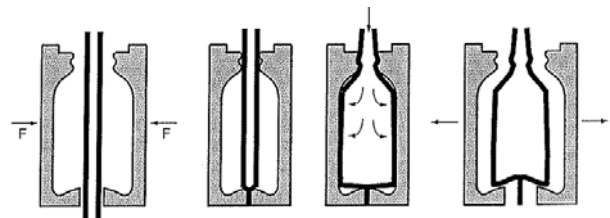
Extrusion-soufflage d'un corps creux (d'après [28])
